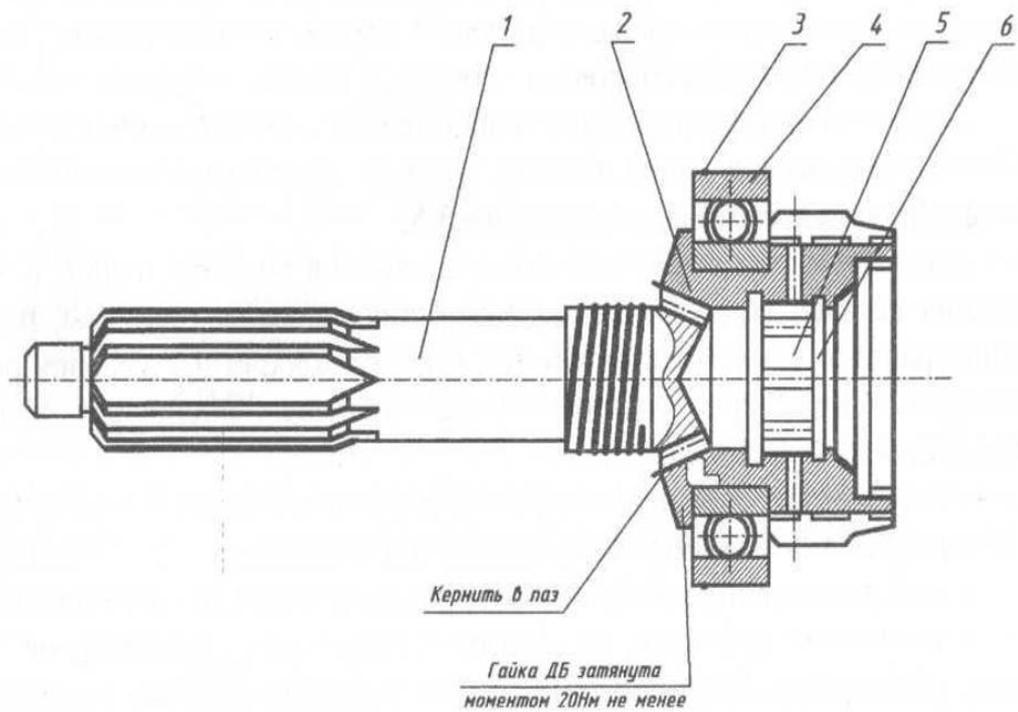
Первичный вал коробки передач автомобиля в сборе
